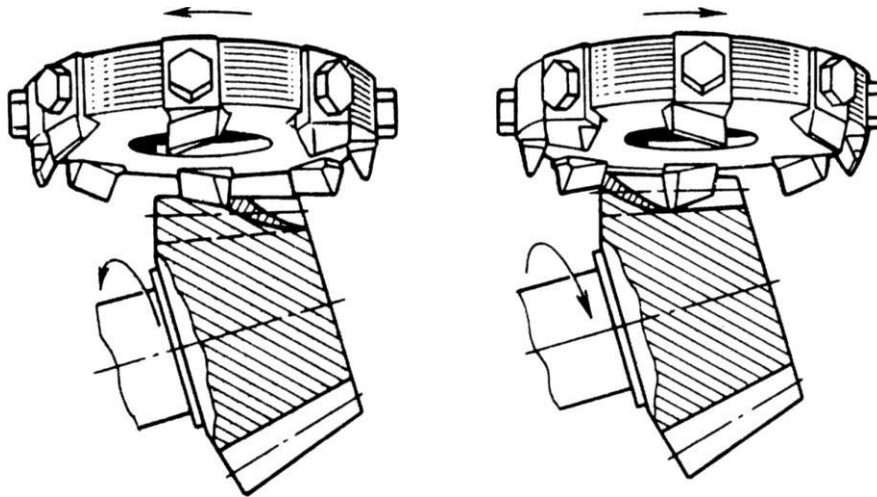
Фрезерування торцевими різцевими головками
